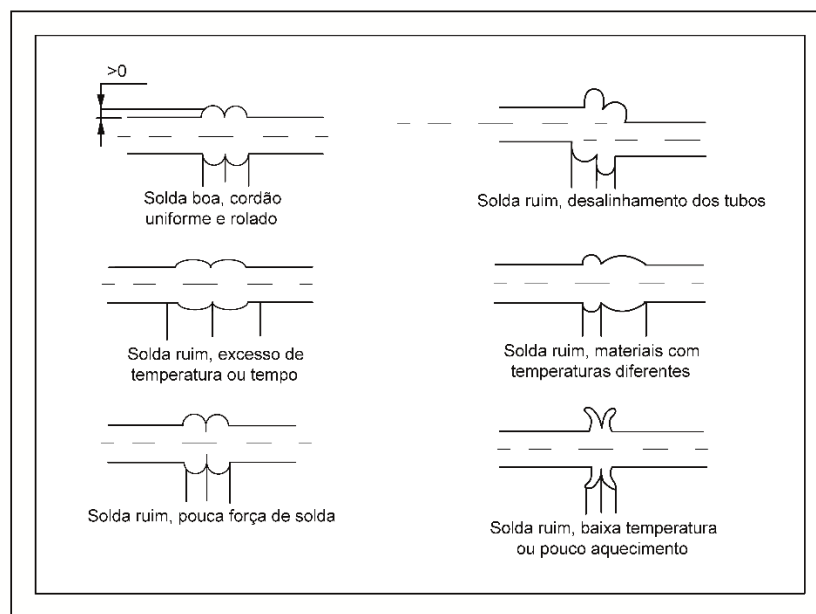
Aspecto típico de uma solda de topo e soldas não conformes
